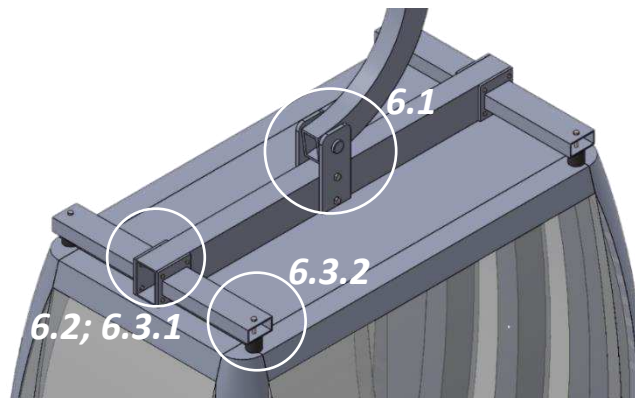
Disegno della struttura con collegamenti da dimensionare.
